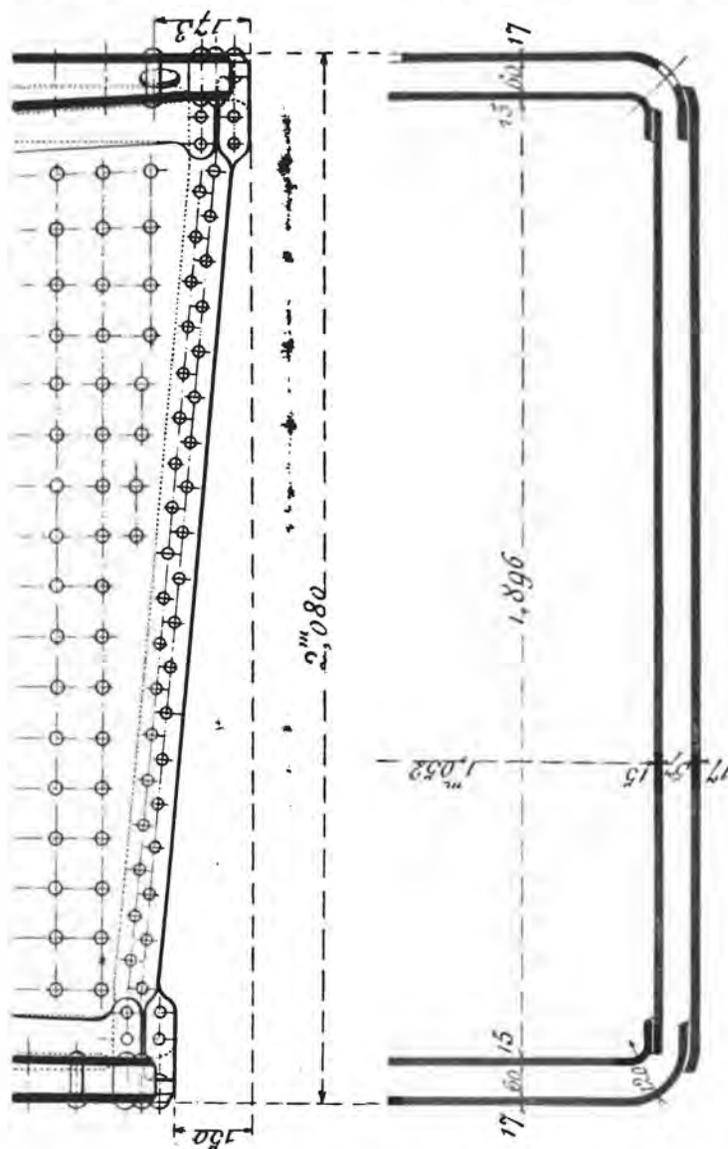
Assemblage des plaques du foyer sur le cadre.
